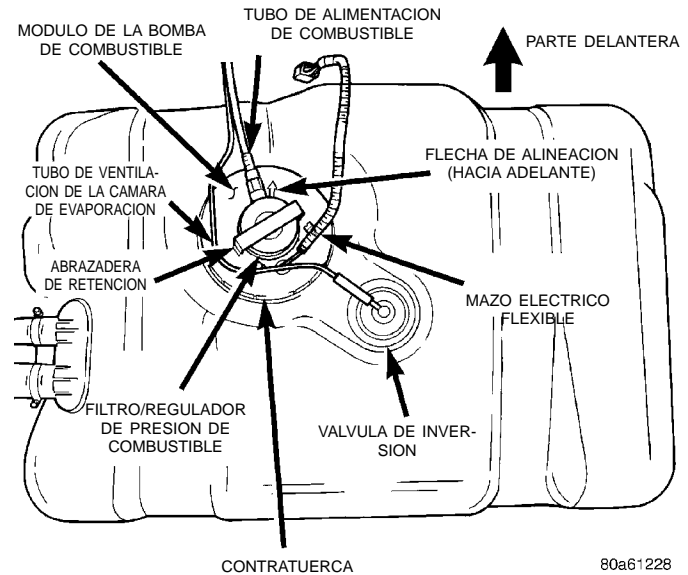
Depósito de combustible/módulo de la bomba de combustible (vista superior)
